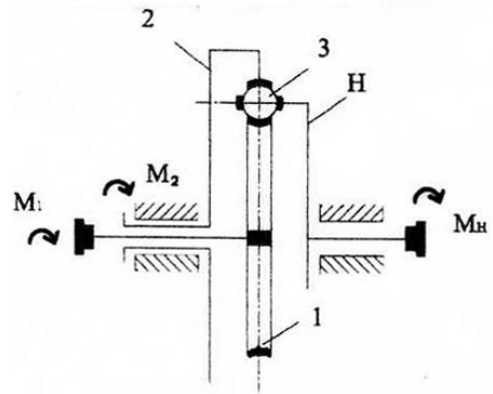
Планетарно-фрикционный механизм на основе шарикового подшипника
